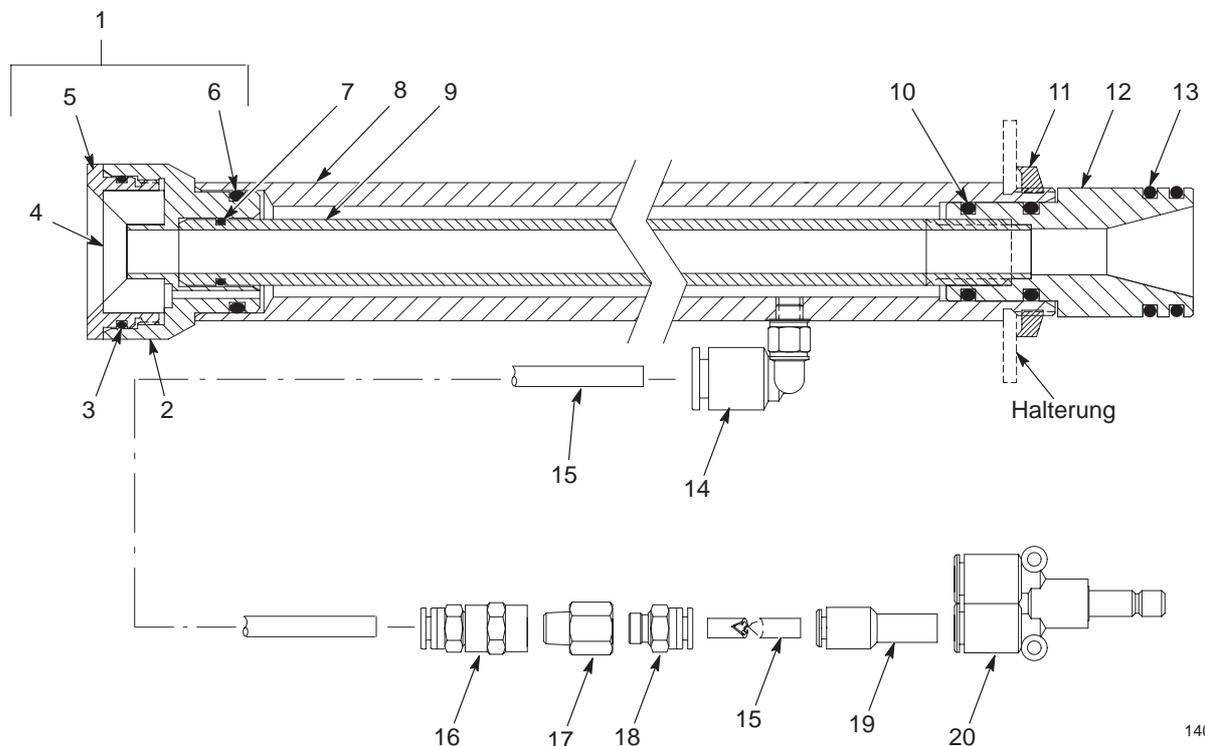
Fluidisierungs-Ansaugrohrsatz mit O-Ring-Befestigung
